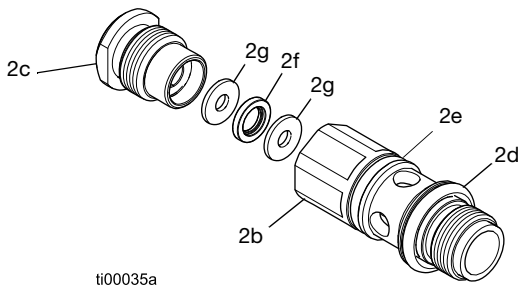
Inserto de fluido y tuerca de empaquetadura
